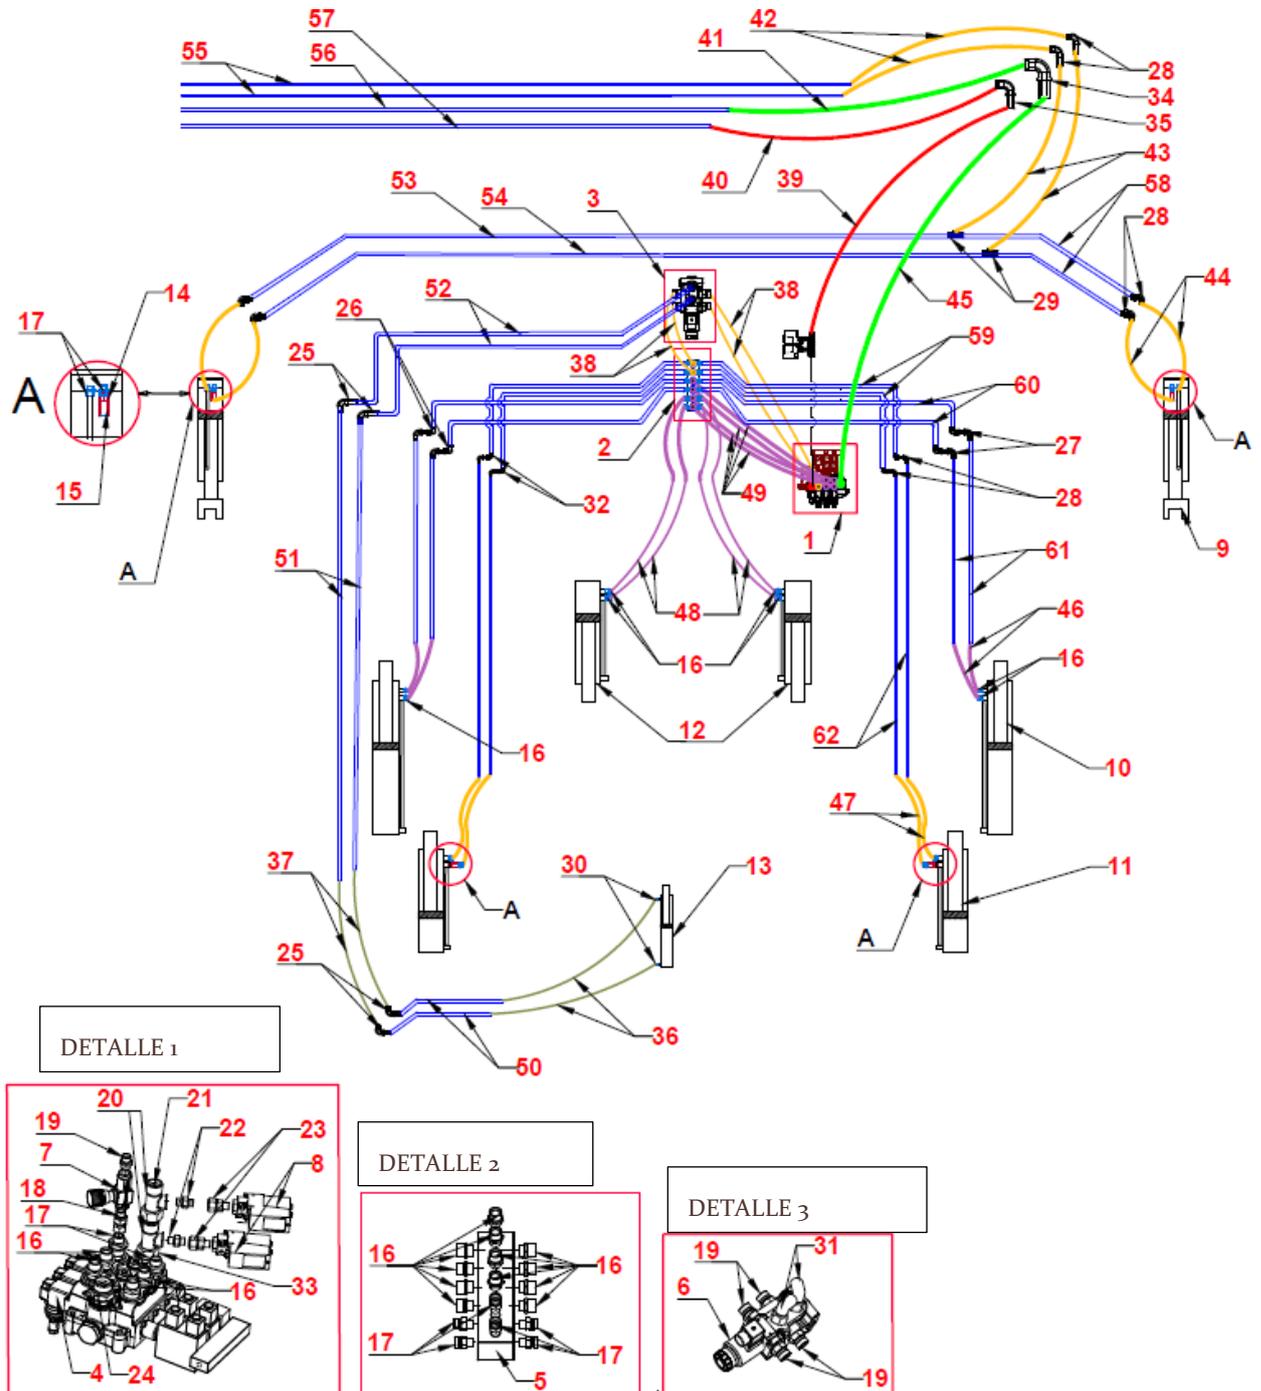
Las Conexiones Hidráulicas de los Equipos de la cubierta posterior
